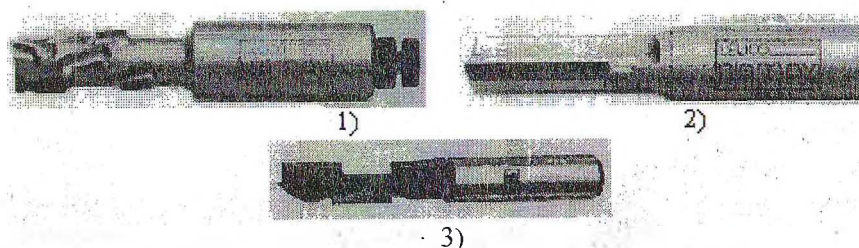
Фрезы концевые для обработки кромок облицованных ДСтП
